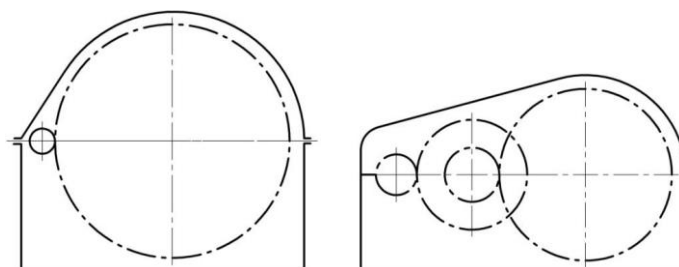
Сравнение габаритов одноступенчатых и двухступенчатых цилиндрических зубчатых редукторов (передаточное число одинаковое)
